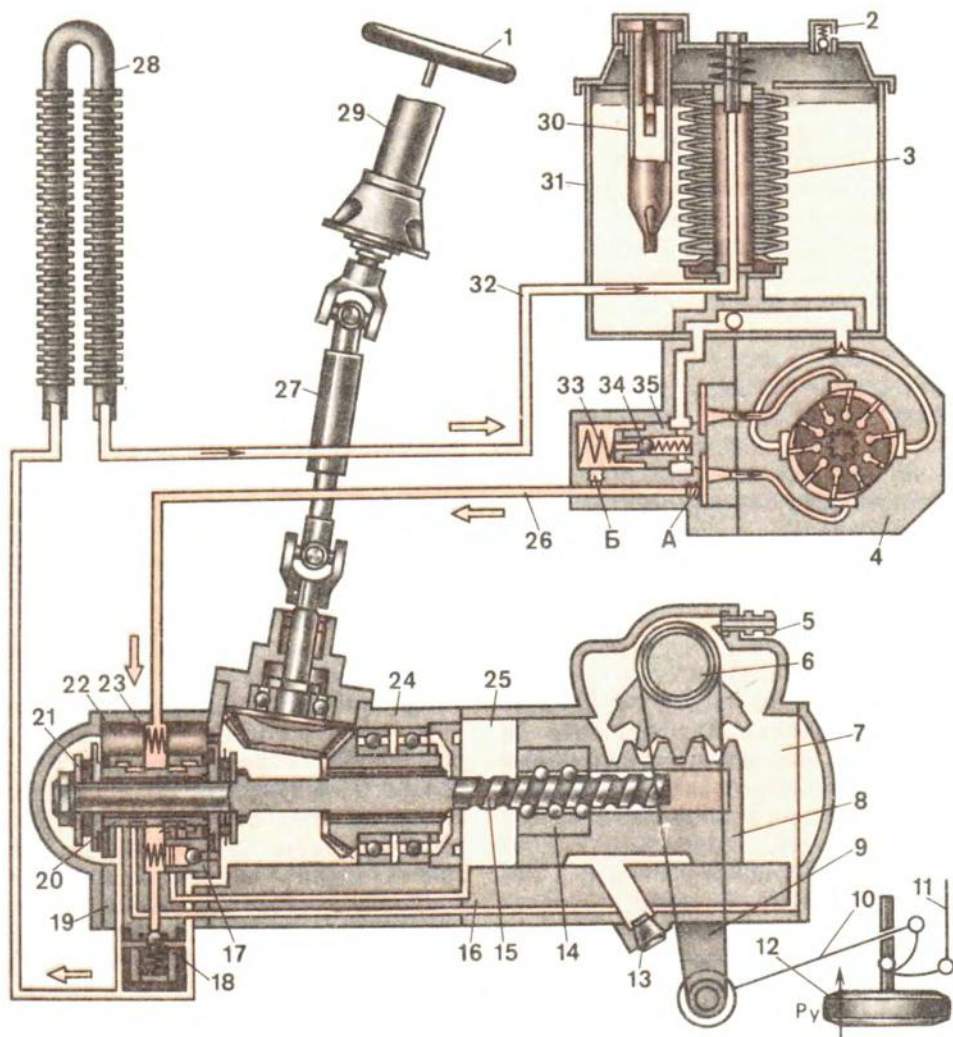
Схема гидроусилителя рулевого механизма автомобилей КамАЗ:
